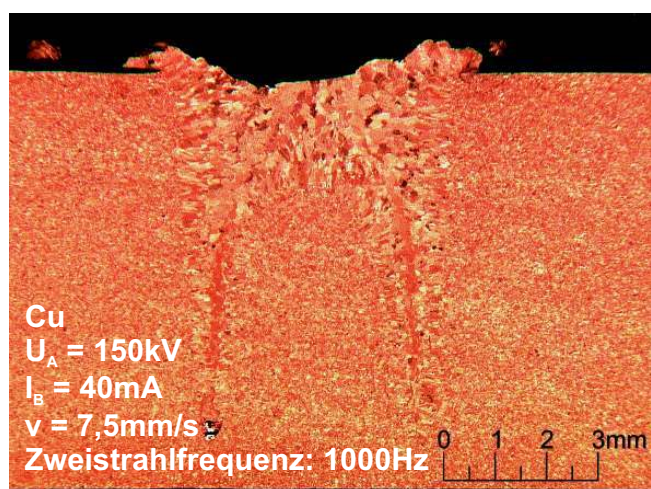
Querschnitt einer Cu-Zweistrahlschweißung
